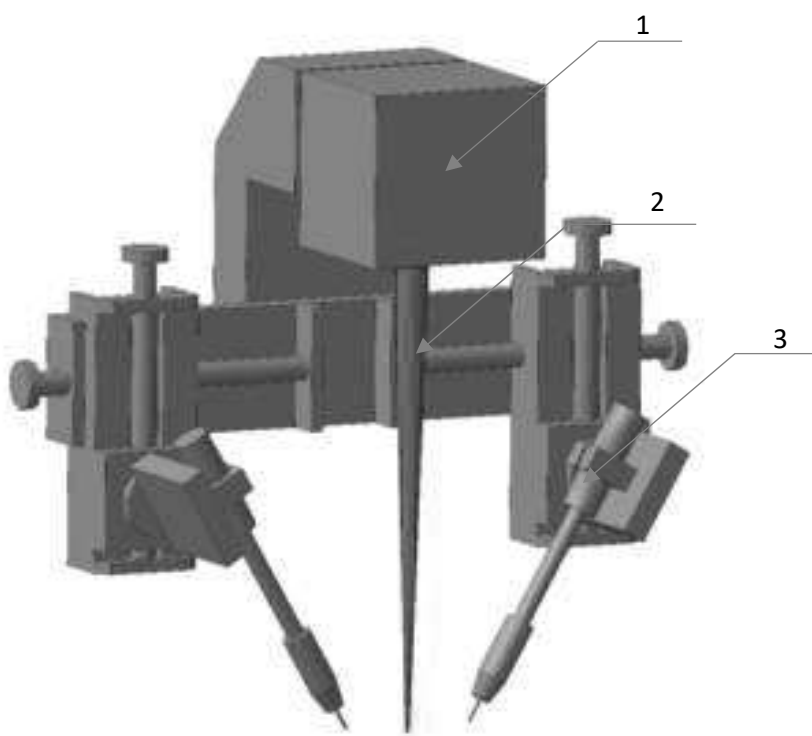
Система для сварки, 1 – лазерная оптическая сварочная головка, 2 – лазерный луч, 3 – электрическая сварочная горелка
